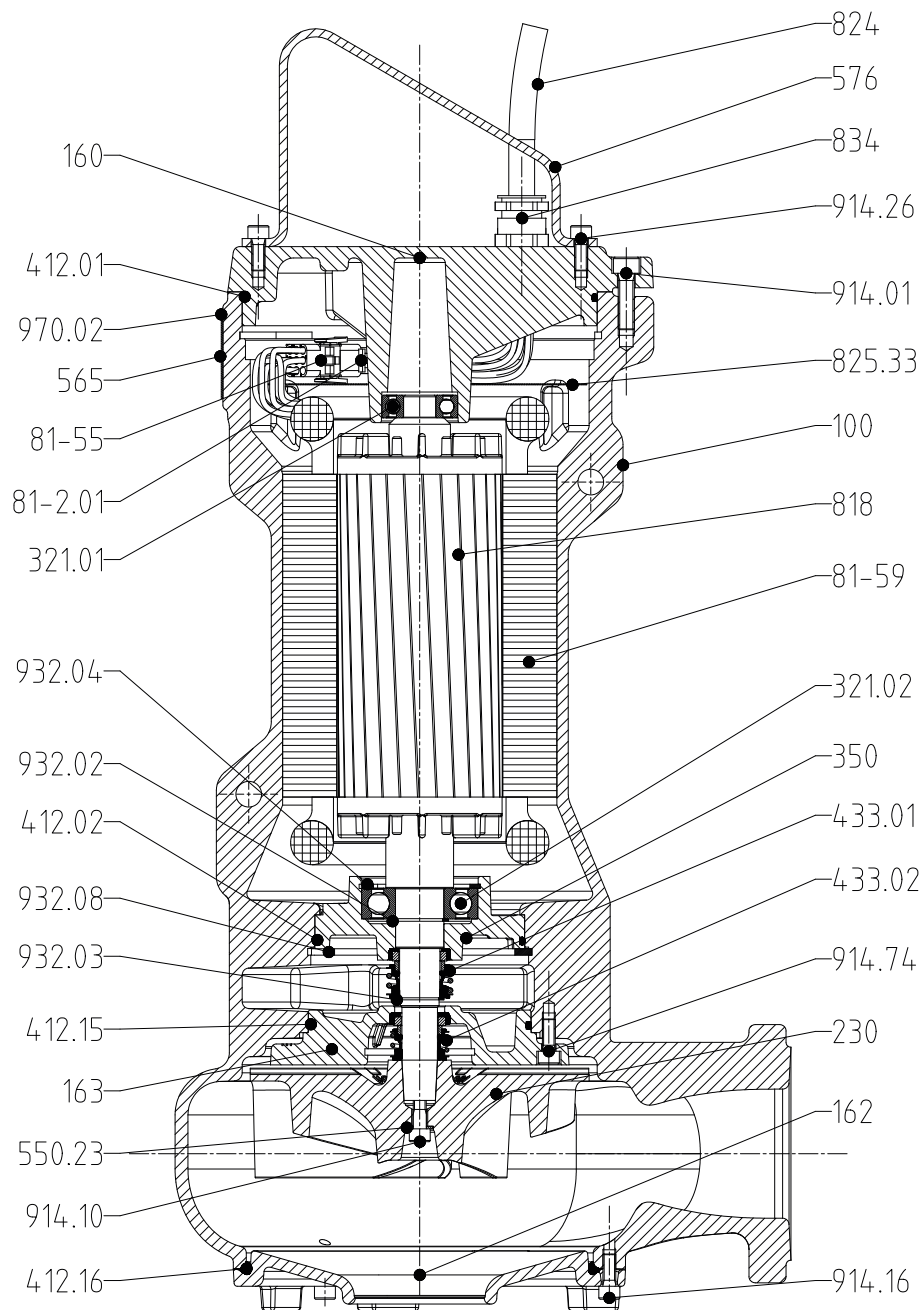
Gesamtzeichnung Ausführung US, mit Laufrad F-max
